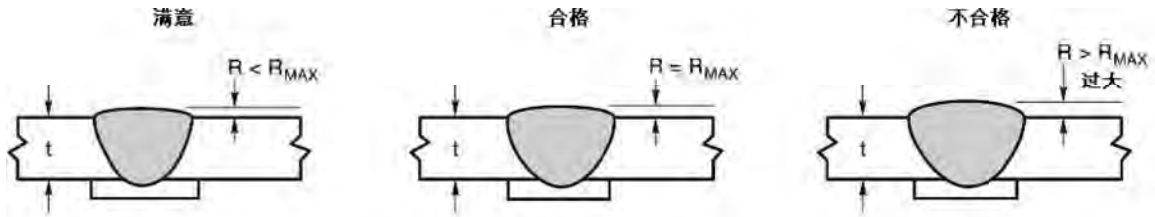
图 A - 对接接头的焊缝外形要求 (参见表2和表3)
